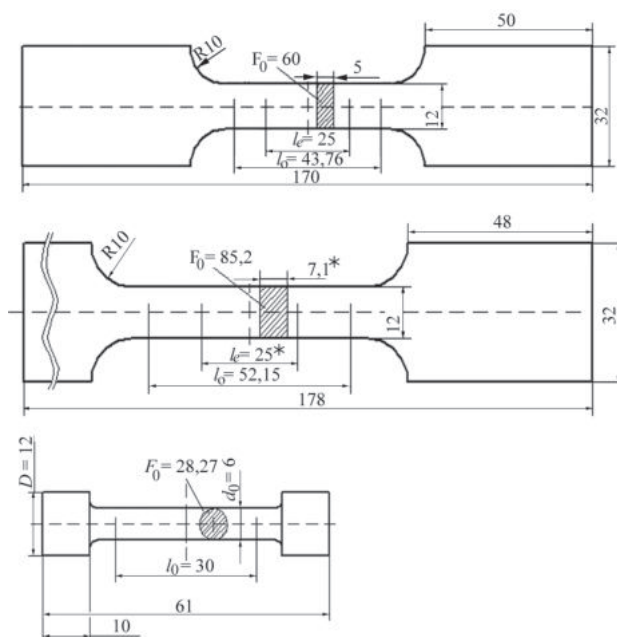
Зразки для випробувань на розтяг: а – плоский з обробкою поверхонь (5×12 мм); б – плоский без обробки поверхонь (7×12 мм); в – циліндричний (МІ-12); l_0 – початкова розрахункова довжина відповідно до тензометра; l_0 – початкова розрахункова довжина; F_0 – початкова площа поперечного перерізу
